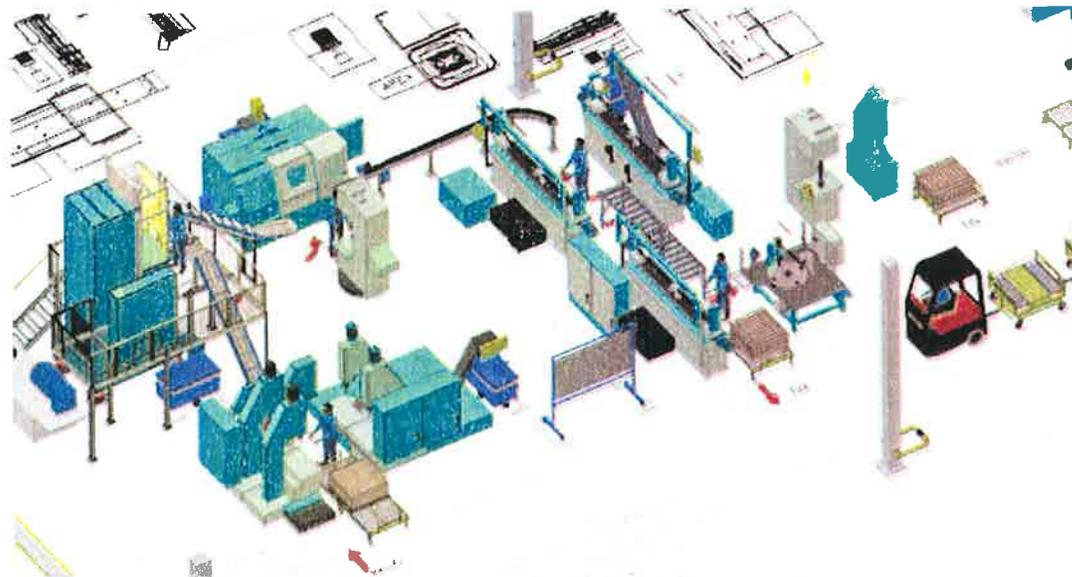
Imagen de CAD en 3D de la línea 74.
